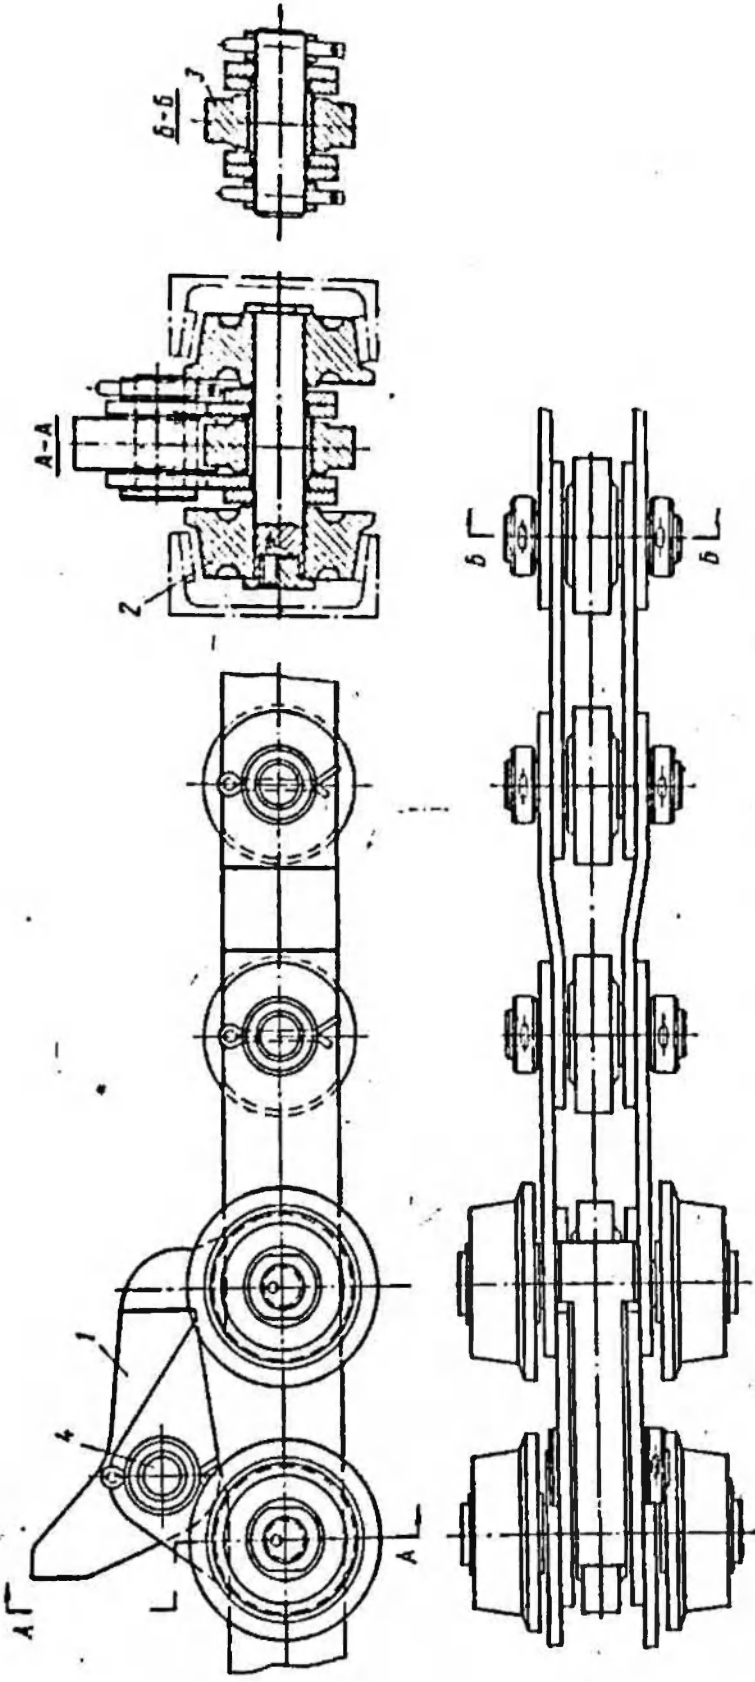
Детали рабочей цепи толкателя ПЭГ-3
